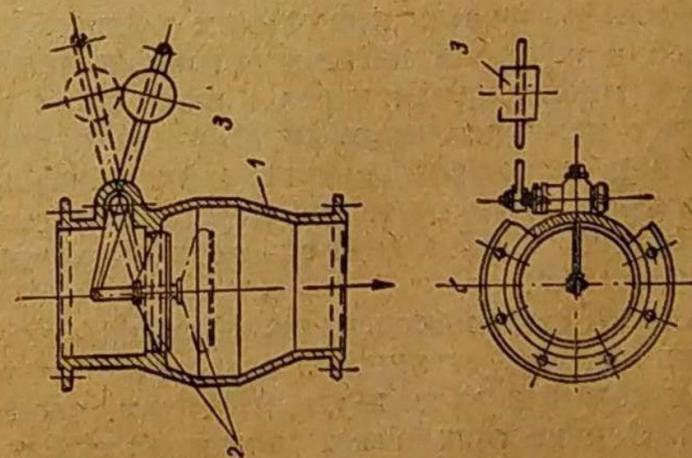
Обратный клапан сухой: 1—корпус, 2—конус, 3—противовес.
